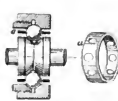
Kugel-Lager mit getrennten Kugeln.
